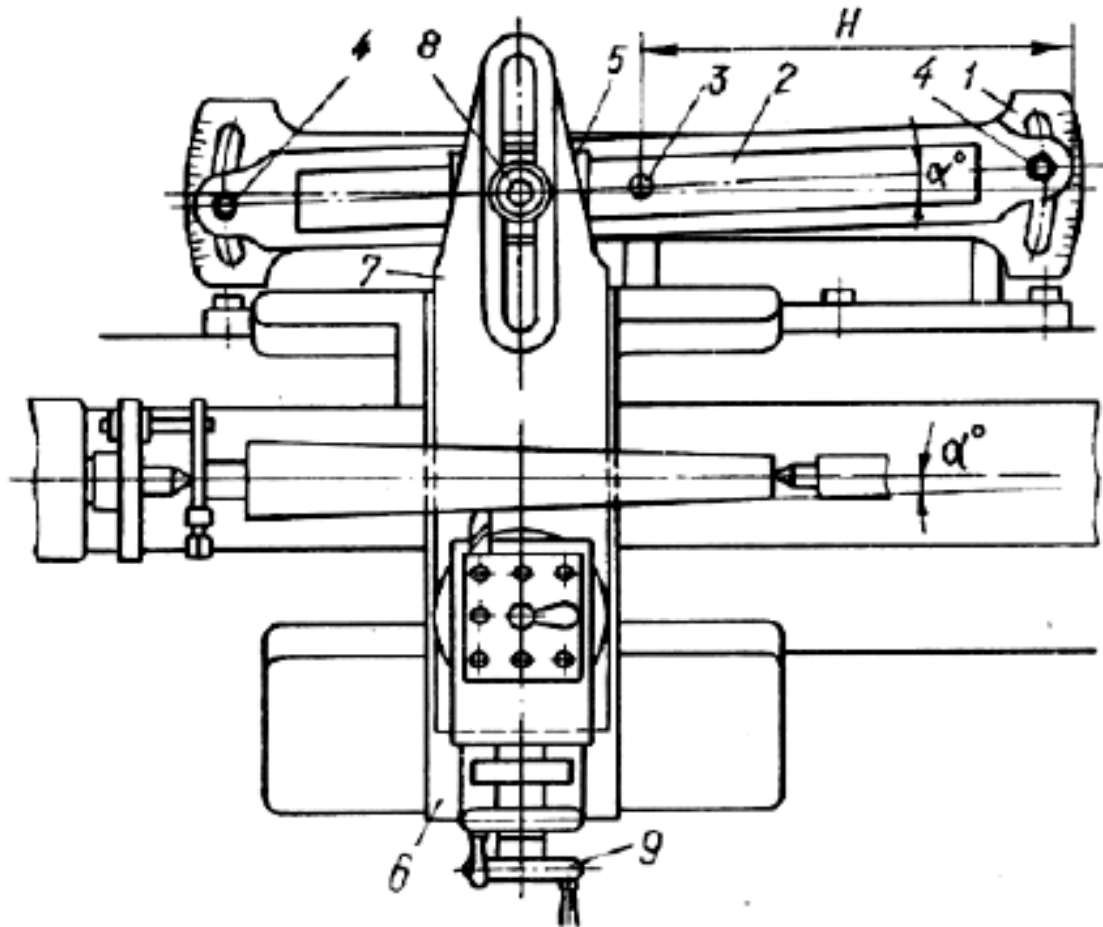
Конусна лінійка: 1 – плита; 2 – лінійка; 3 – палець; 4 – гвинти; 5 – повзун; 6 – супорт; 7 – тяга; 8 – затискач; 9 – рукоятка
